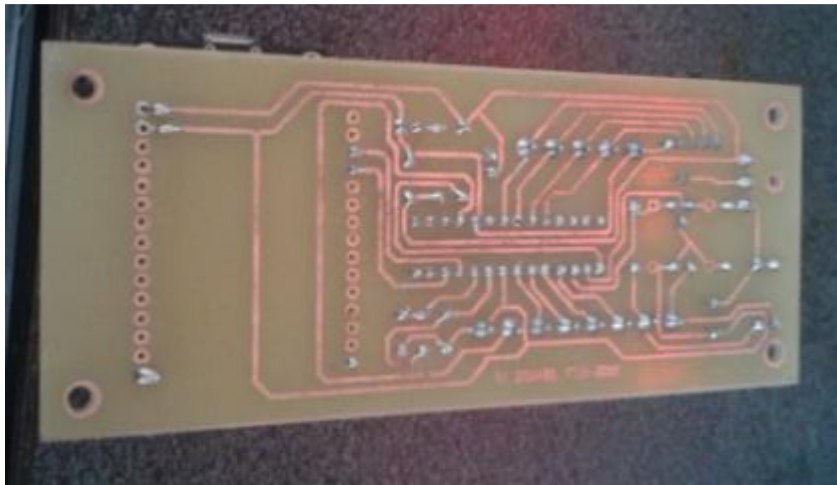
4. Pista y soldaduras en placa de control.
